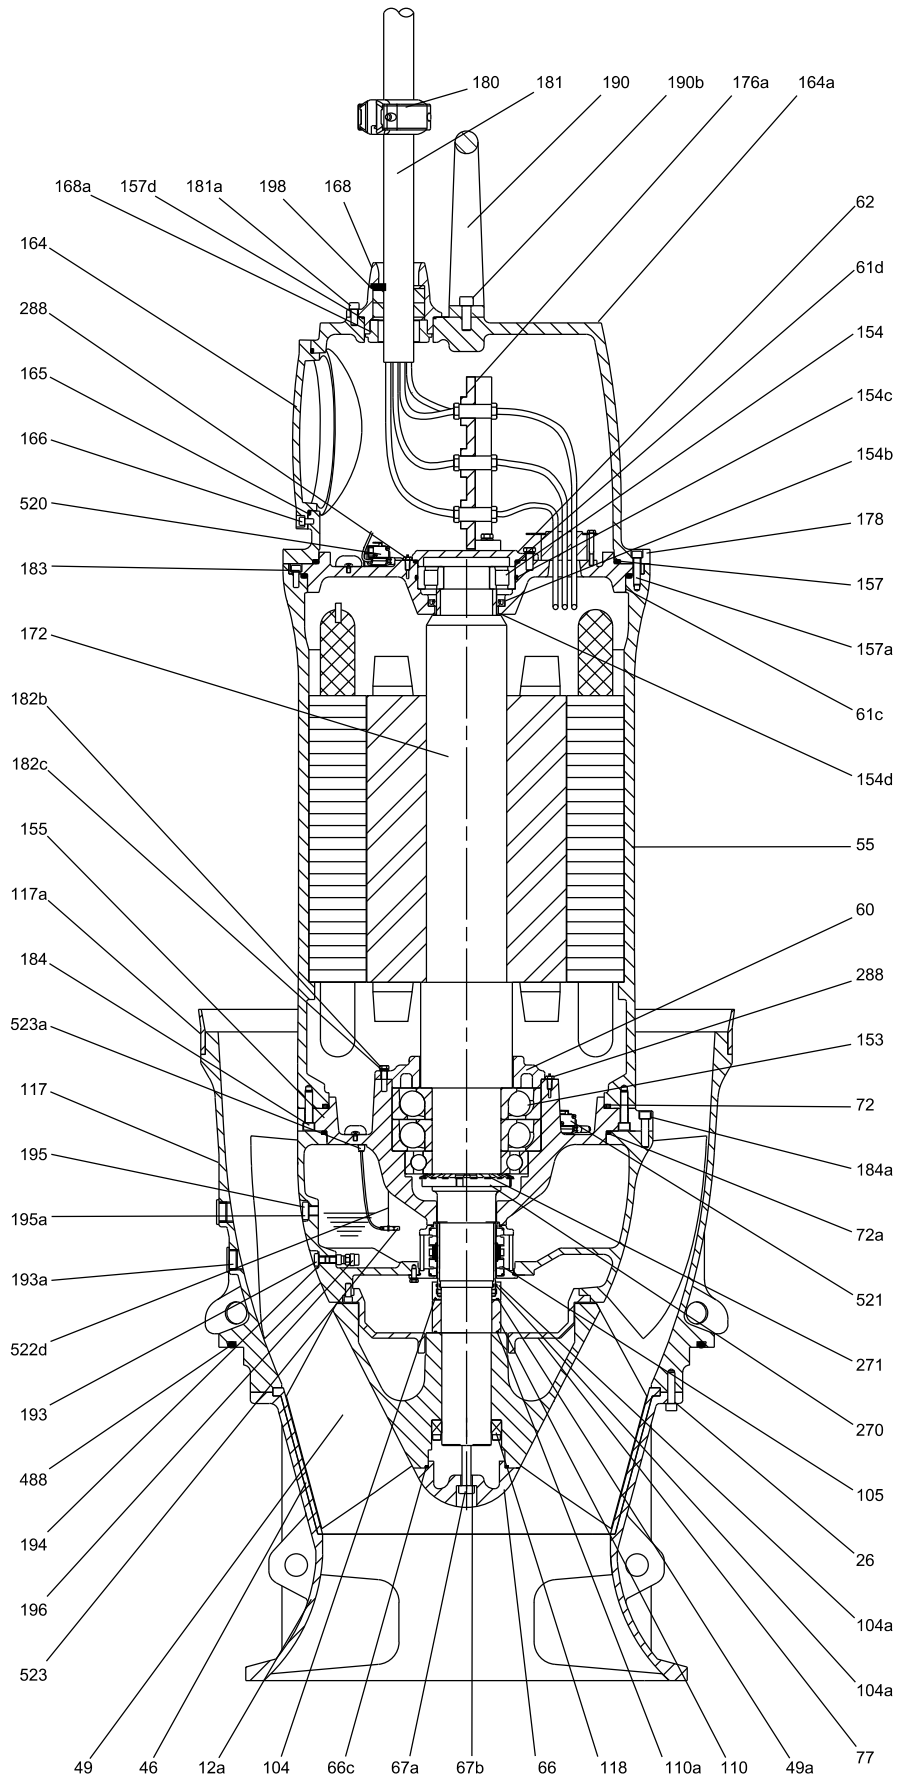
Чертеж в разрезе, KWM, обсадная труба диаметром 800-1600
